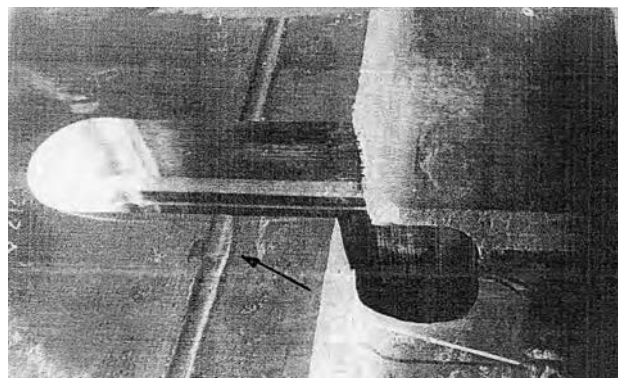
Вид разделки (длина 960, ширина 120, глубина - 1 200 мм) после удаления трещин, образовавшихся при возобновлении процесса электрошлаковой сварки (стрелкой показано место остановки процесса) станины гидравлического пресса
